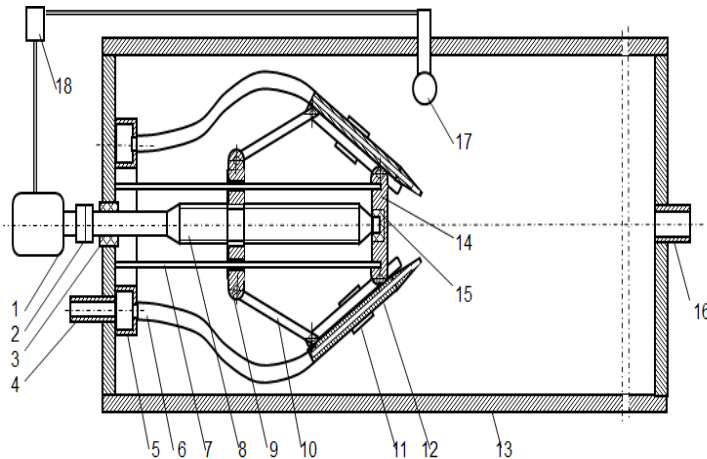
Принципова схема конструкції ГДСК (поздовжній переріз):
